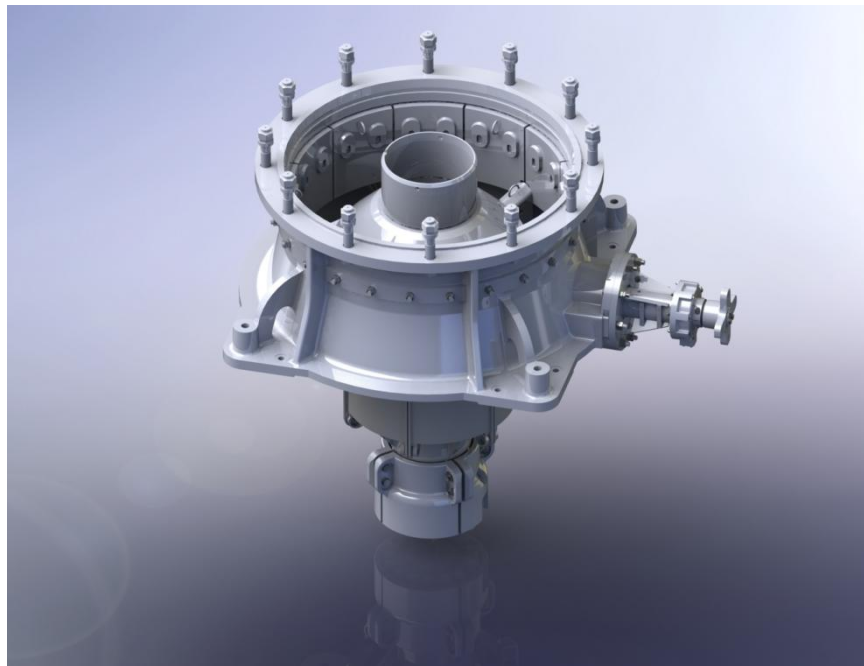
Комп'ютерна модель дробарки конусної КРД 700-75
